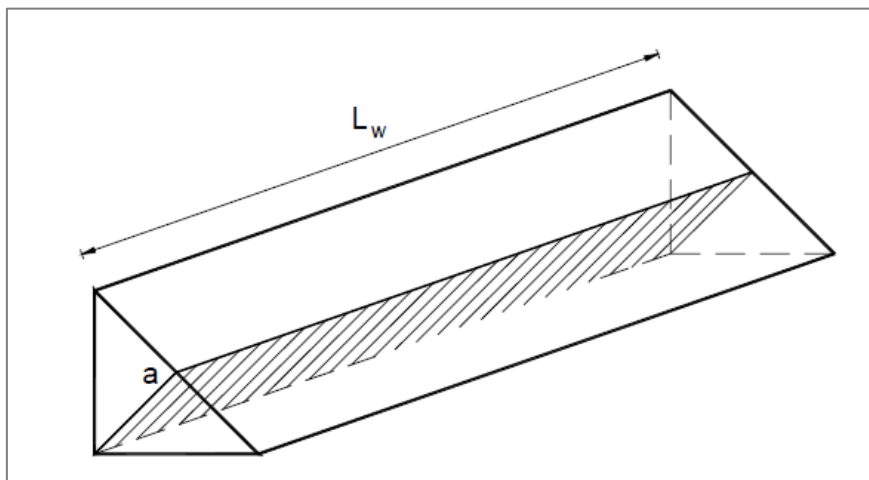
44: Dimensiones del cordón de soldadura a, L. (Guardiola, 2 011)
